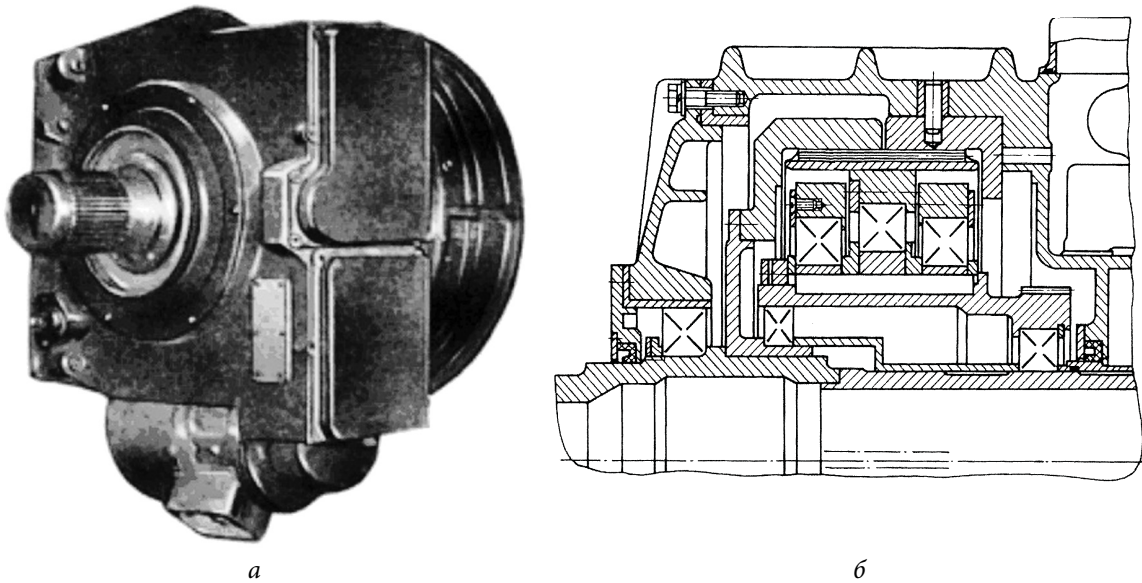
Внешний вид (а) и конструктивная схема (б) высокомоментного привода
